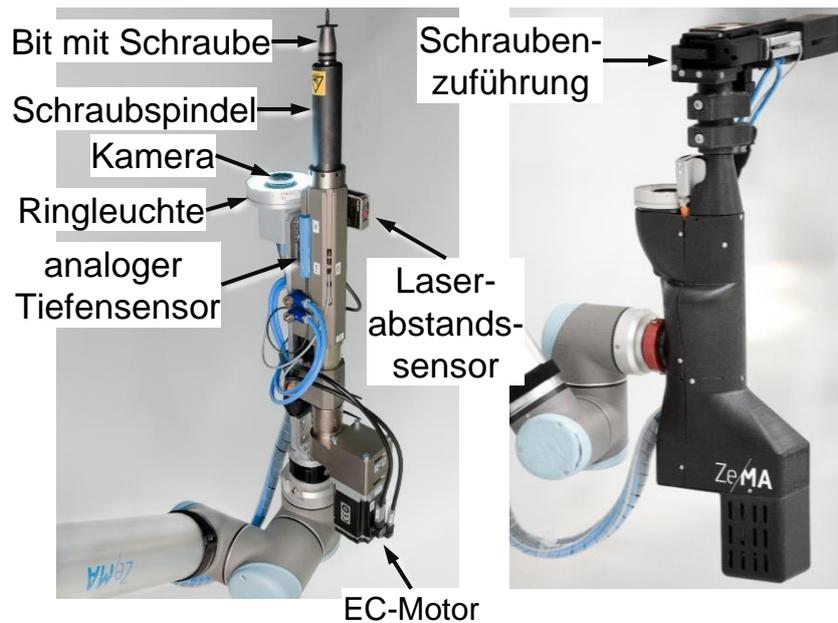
Endeffektor mit Werkzeug und angebrachter Sensorik
